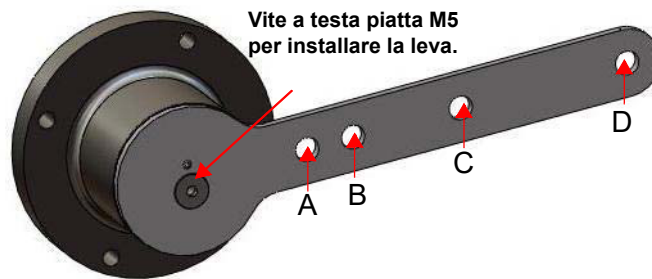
Portamagnete e leva standard per valvole a movimento alternato
